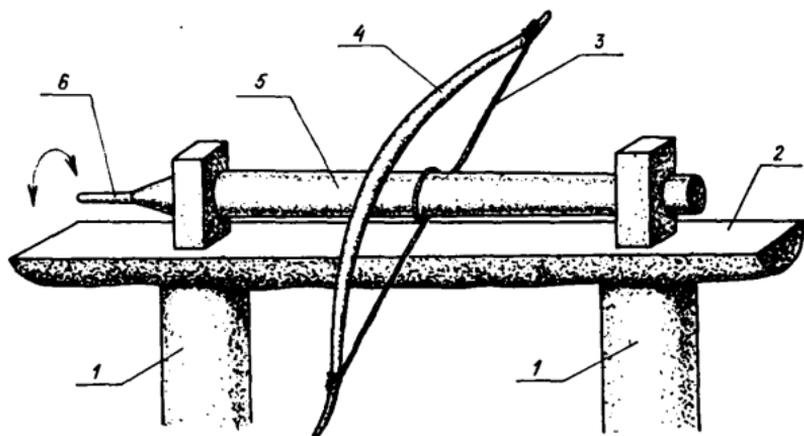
Первобытный сверлильно-токарный станок для цилиндрического сверления каменных пронозков (эксперимент).
